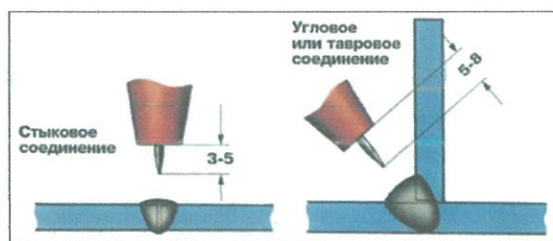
Вылет электрода при TIG сварке
